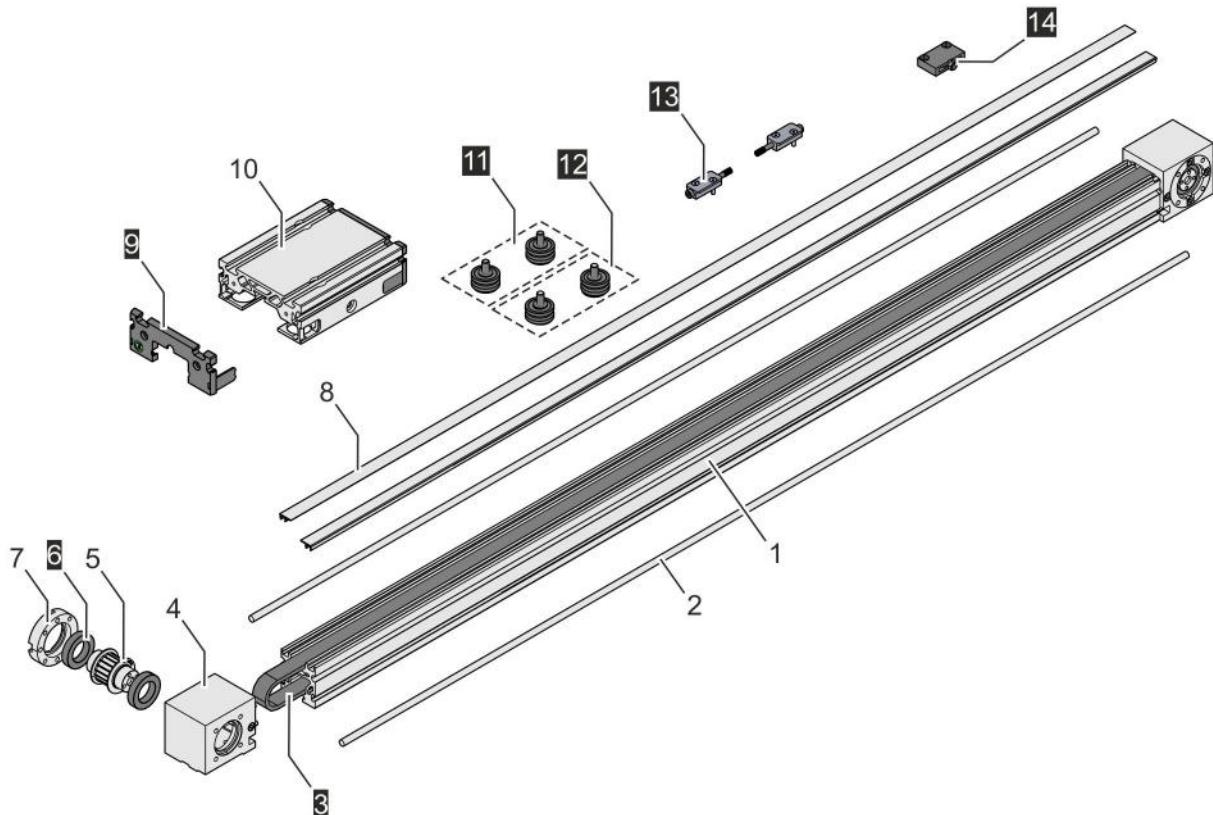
Unité linéaire RK MonoLine Z – vue éclatée
